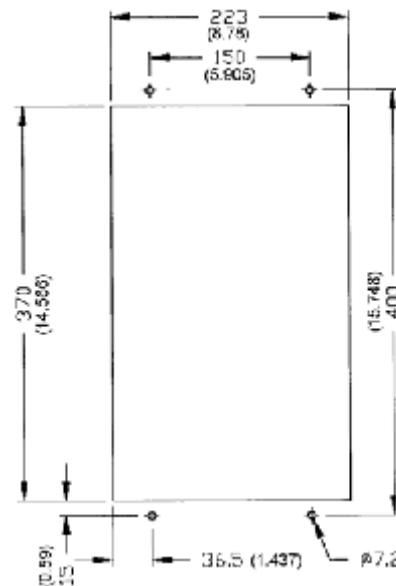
Cutout dimensions in air duct - Dimensiones mm (inch)
